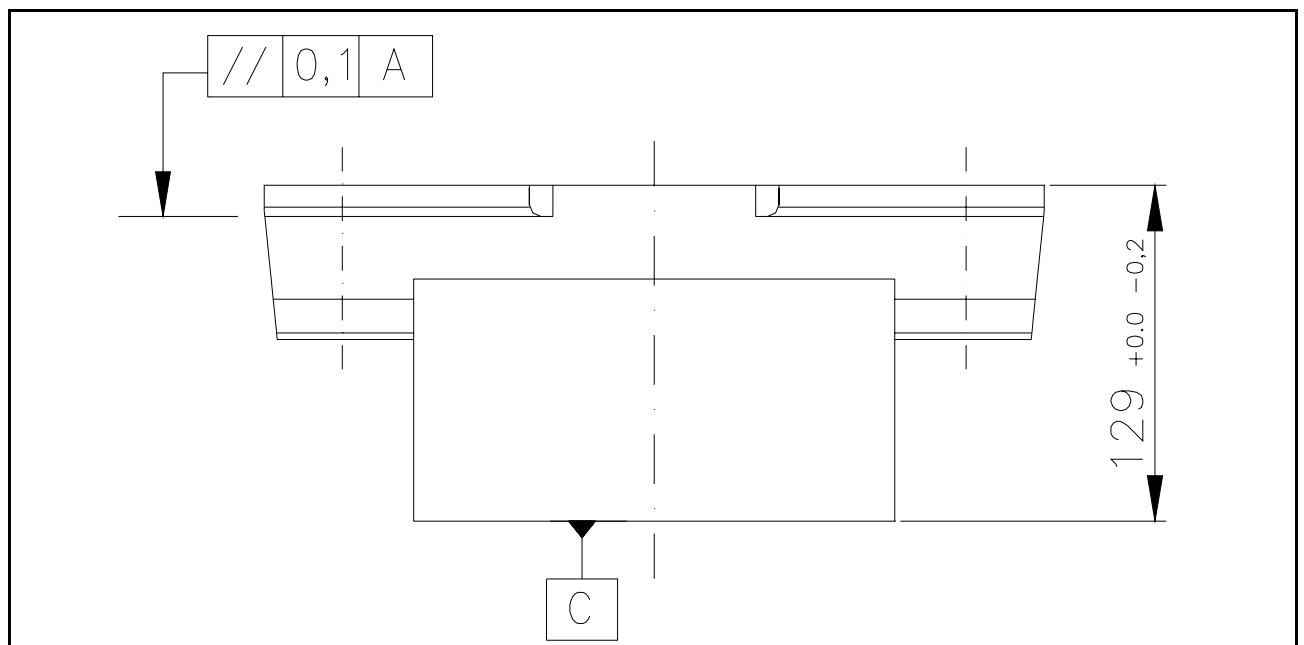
Befestigungsachsen des Statorpaketes (Querschnitt)
